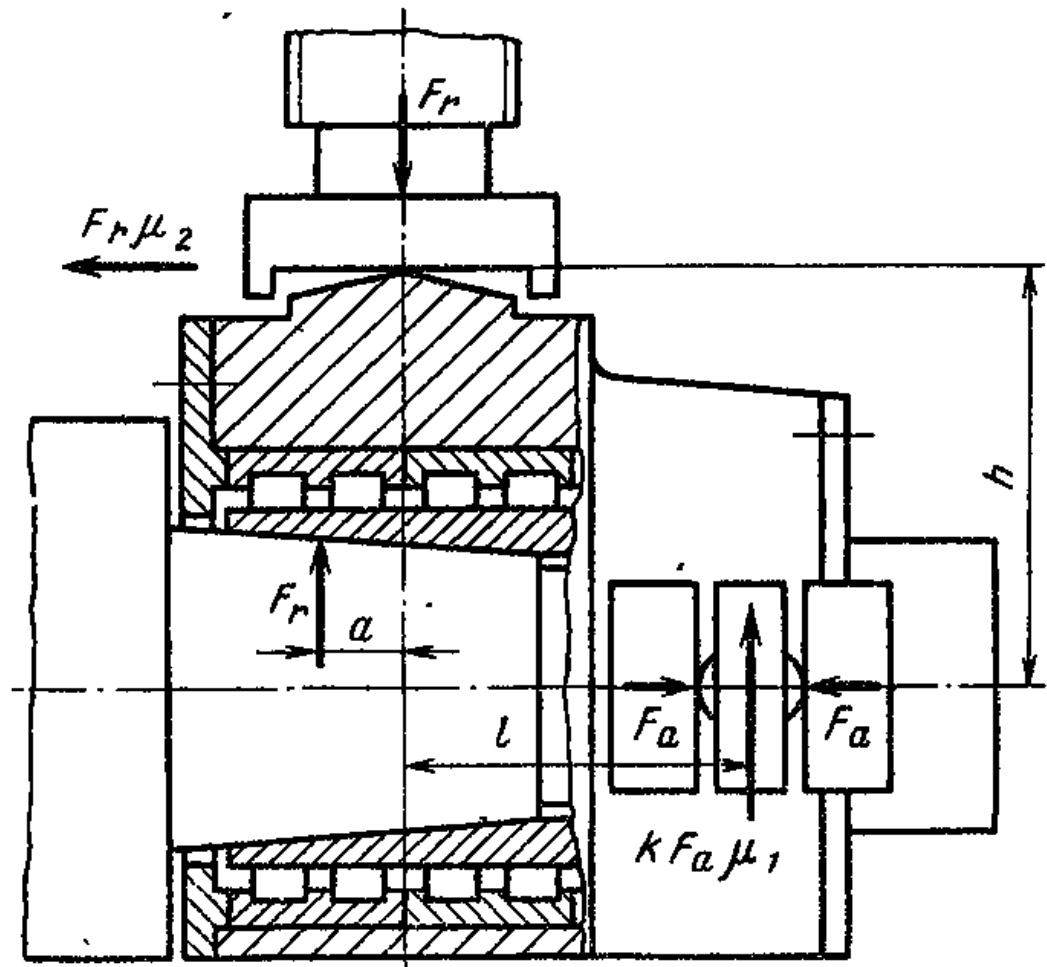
Схема дії сил на підшипники при твердій осьовій фіксації подушки прокатного валка
